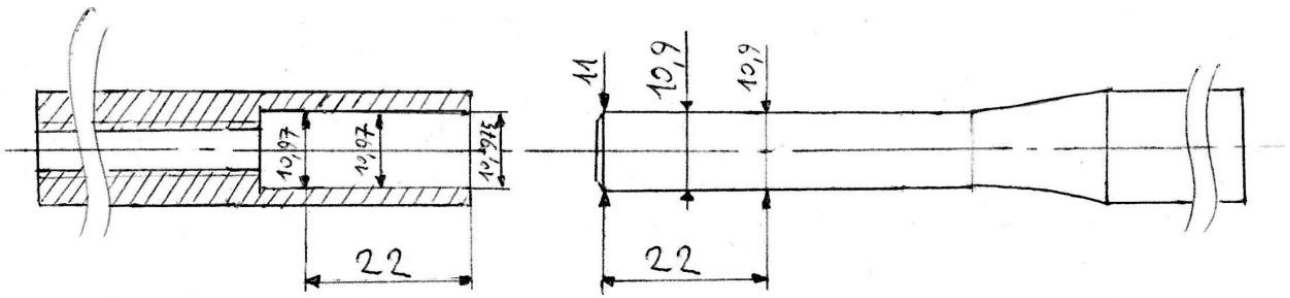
Dimensioni reali del provino campione prima dell'assemblaggio
